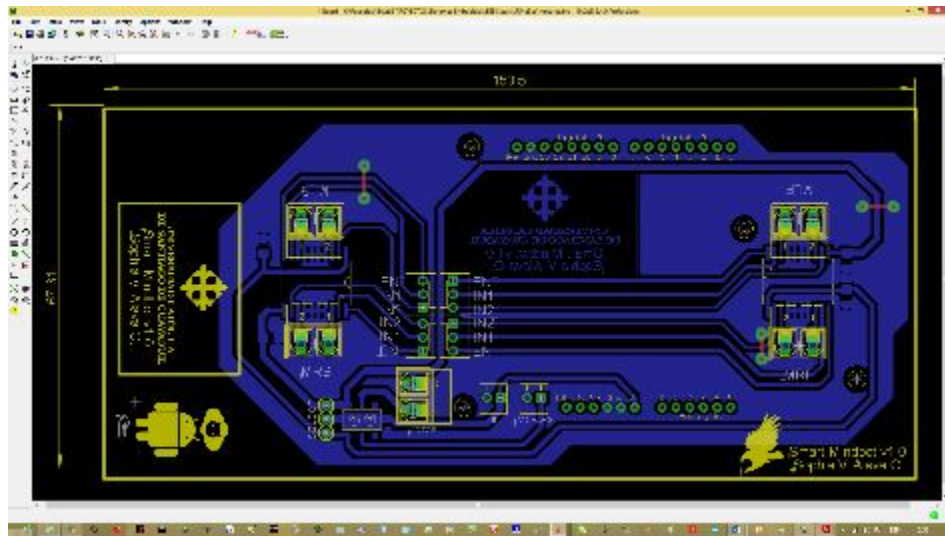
Diseño de la PCB de control de motores usando Eagle CadSoft.
